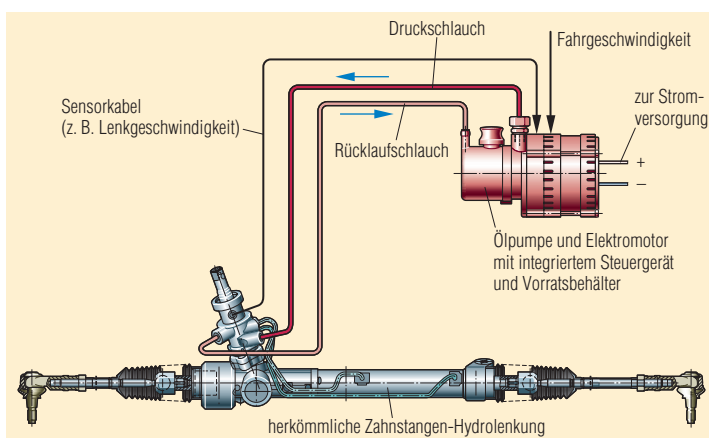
Elektrohydraulische Hilfskraftlenkung.
